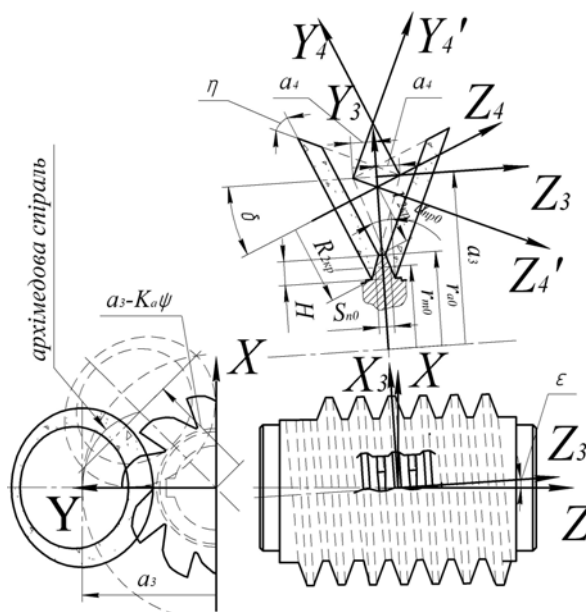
Схема формоутворення бічної сторони зуба фрези при її затилюванні шліфувальним дисковим інструментом
